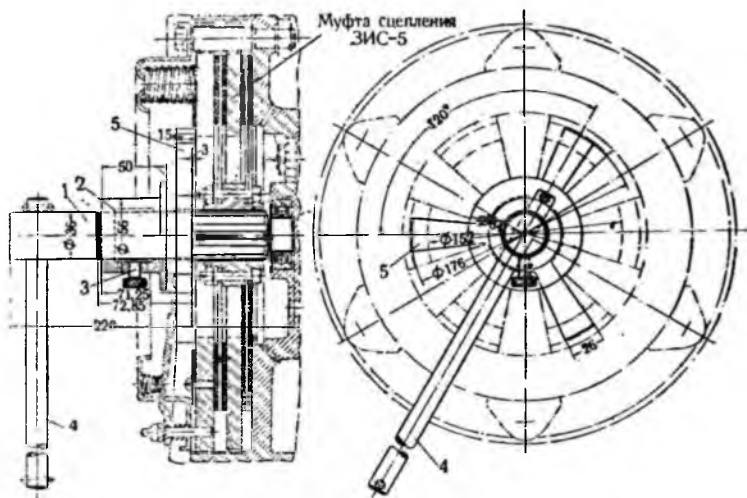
Приспособление для центровки ведомых дисков и для регулировки отжимных рычагов муфты сцепления ЗИС в рабочем положении:
